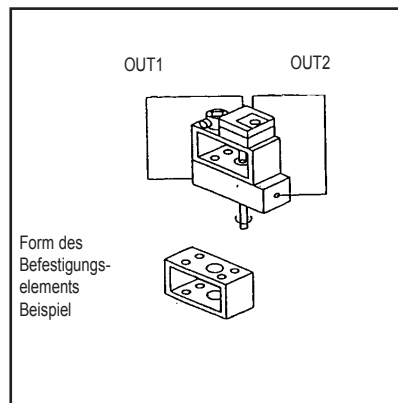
Beispiel für Befestigung hinten am Innengewinde
